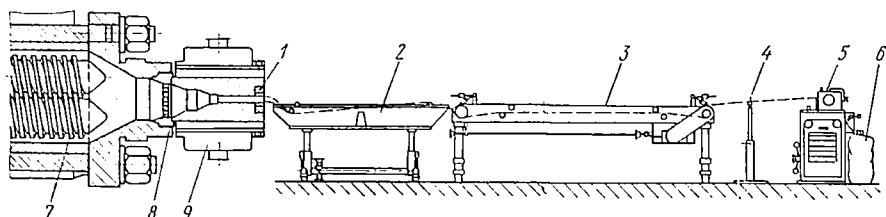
Установка для резки предварительно охлаждаемых прутков
